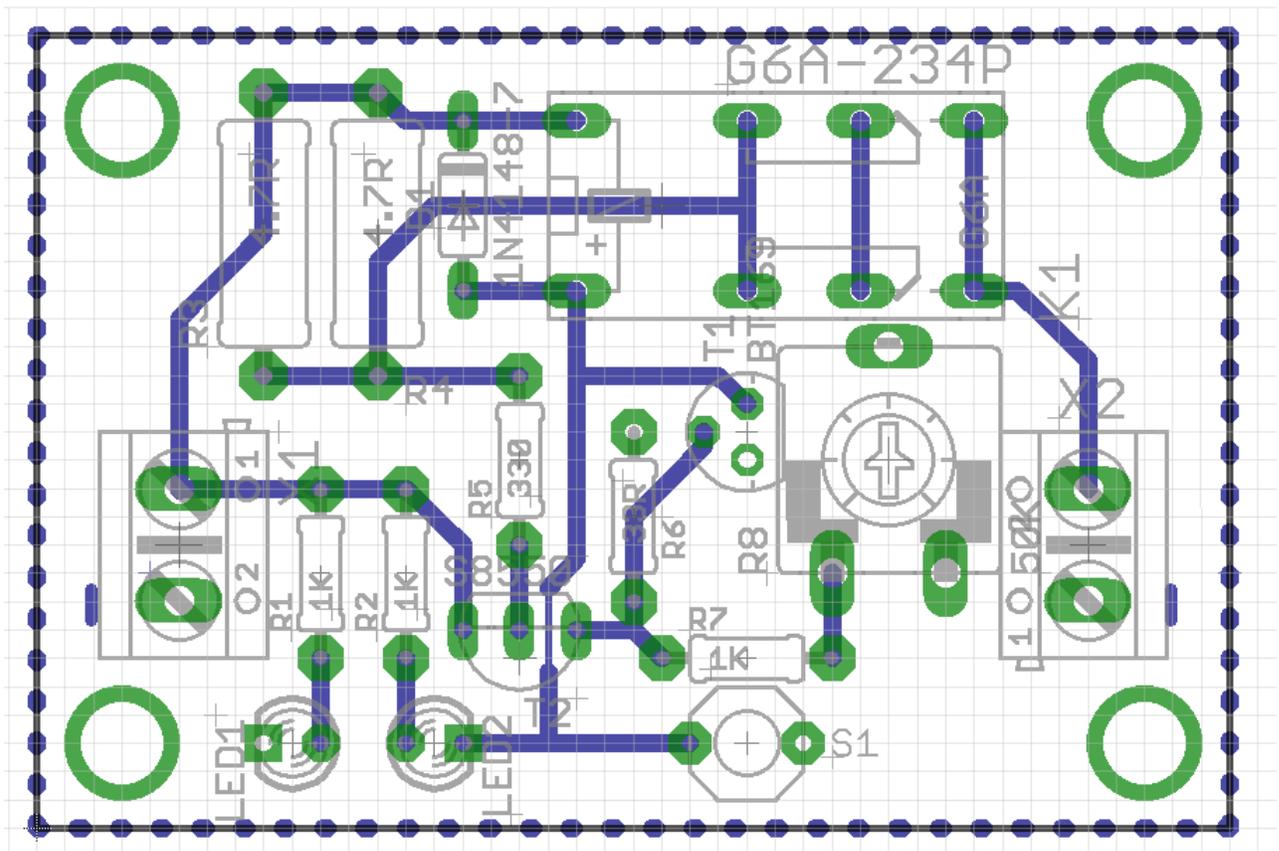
c Diseño del PCB del control del almacenador.
